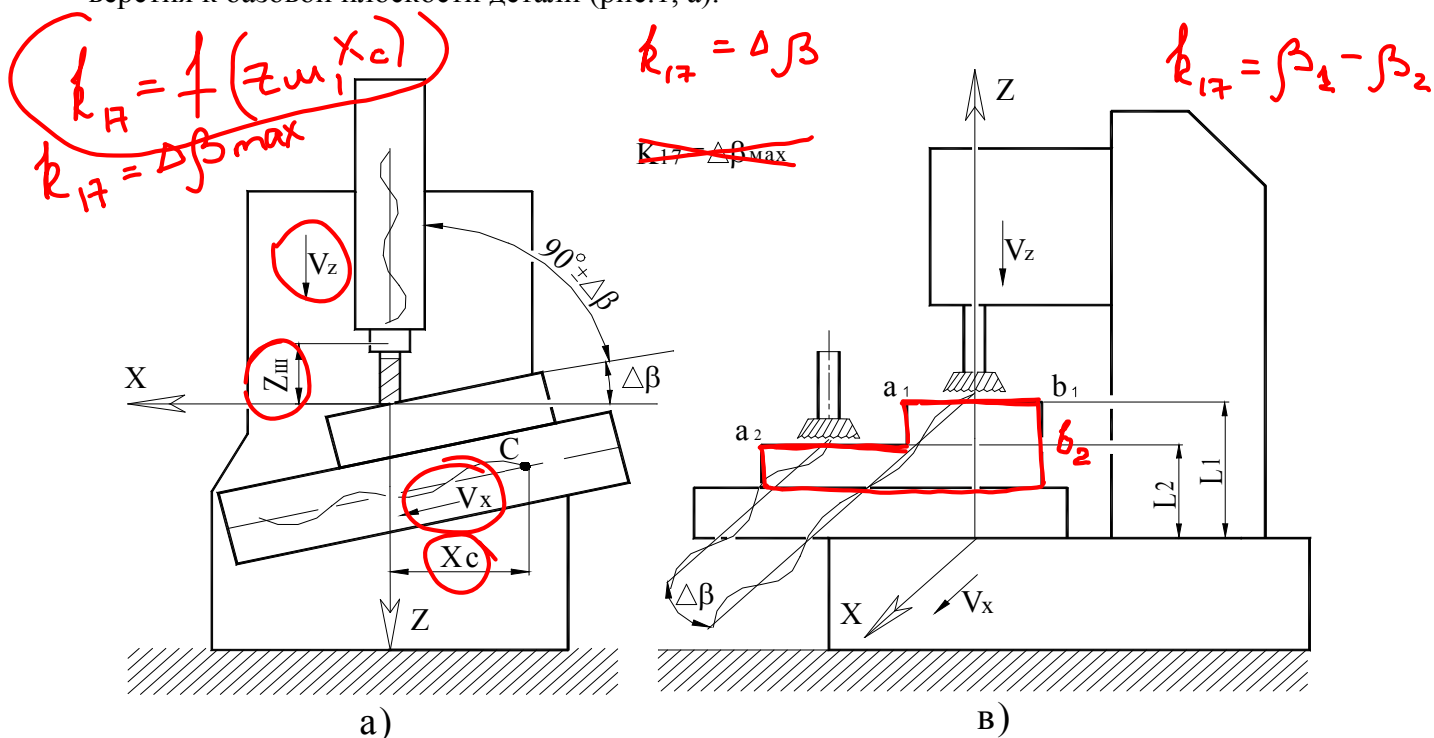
Отклонение положения поверхности для координатно-расточного станка
